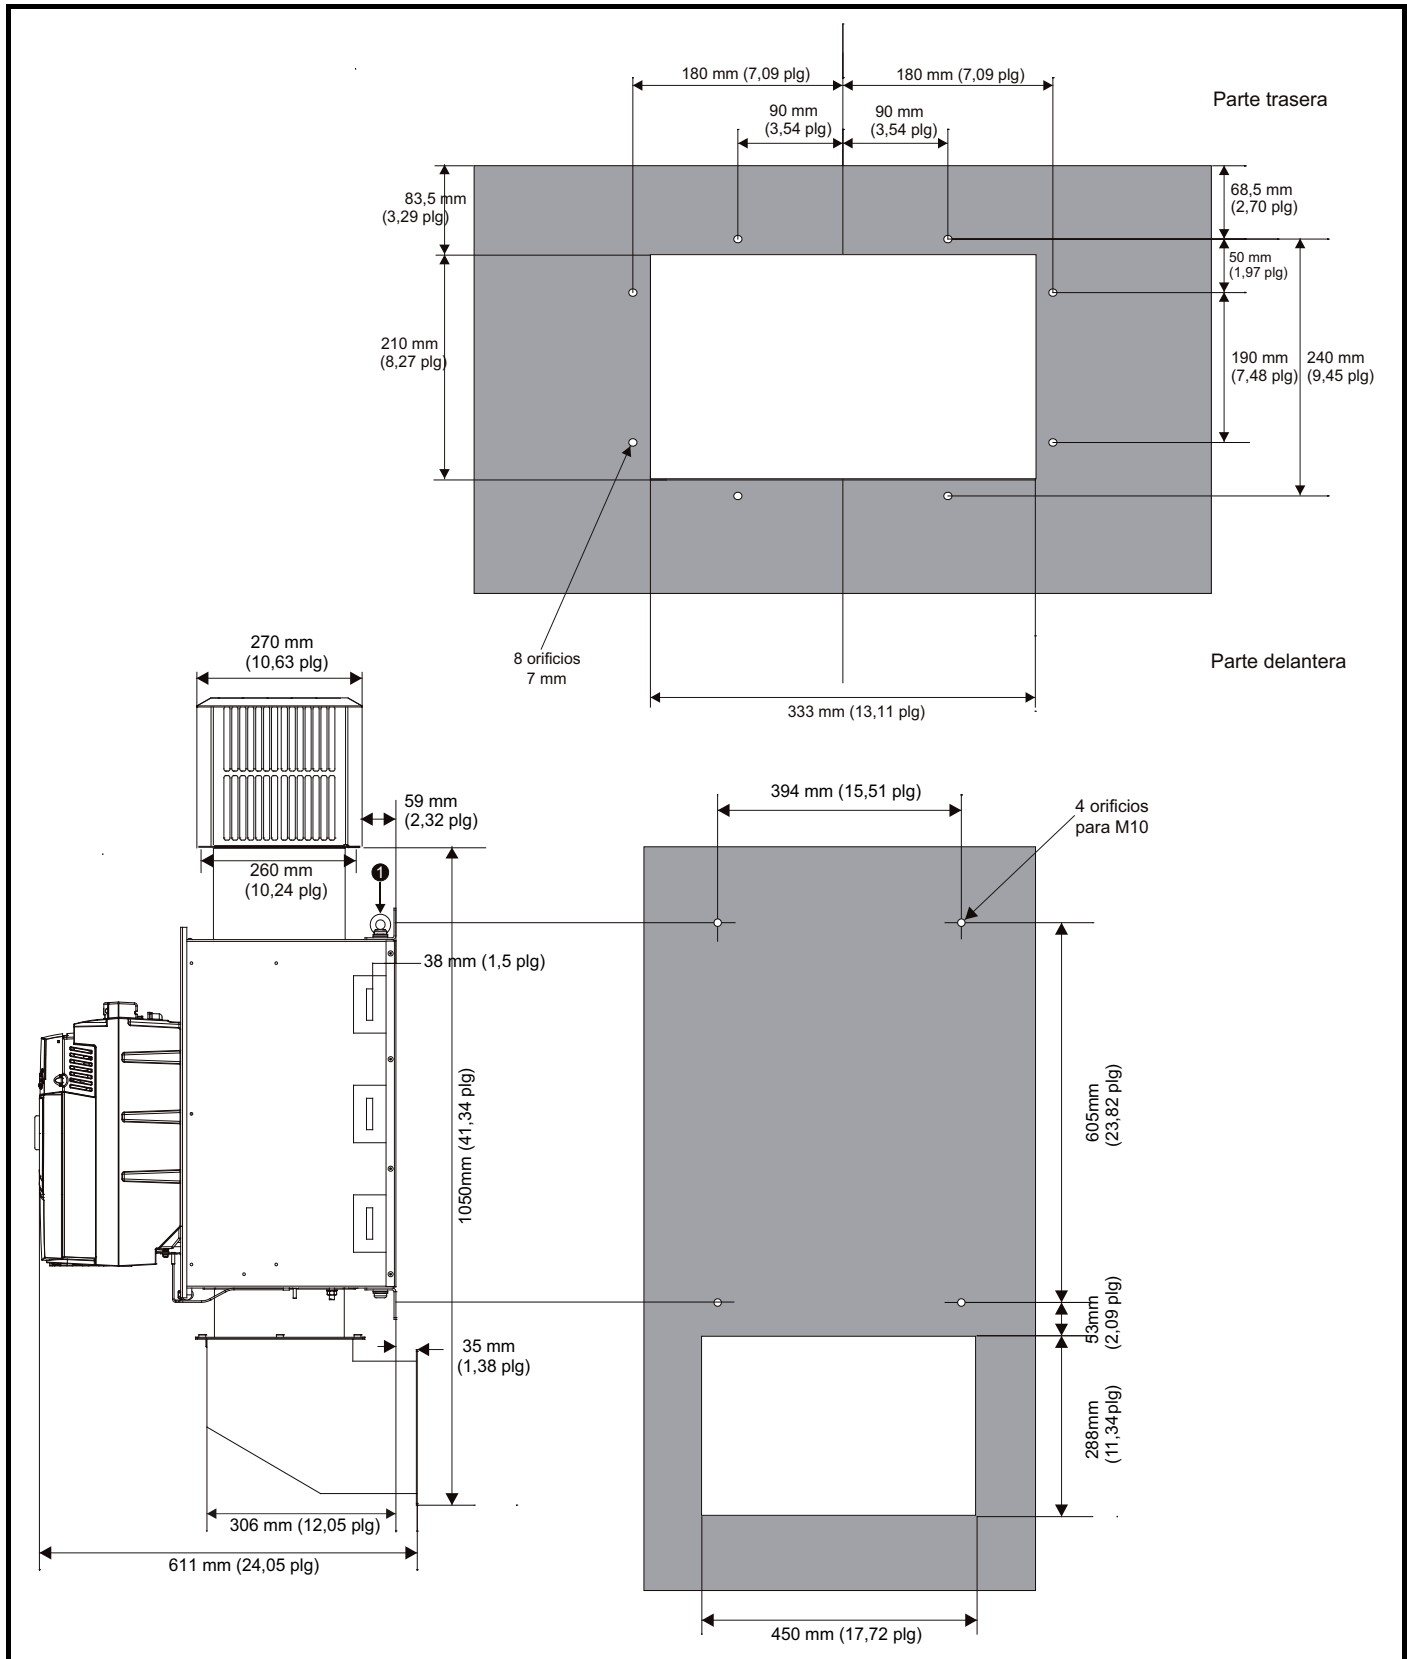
Placa posterior y detalles de montaje de los accionamientos de tamaño 2C
